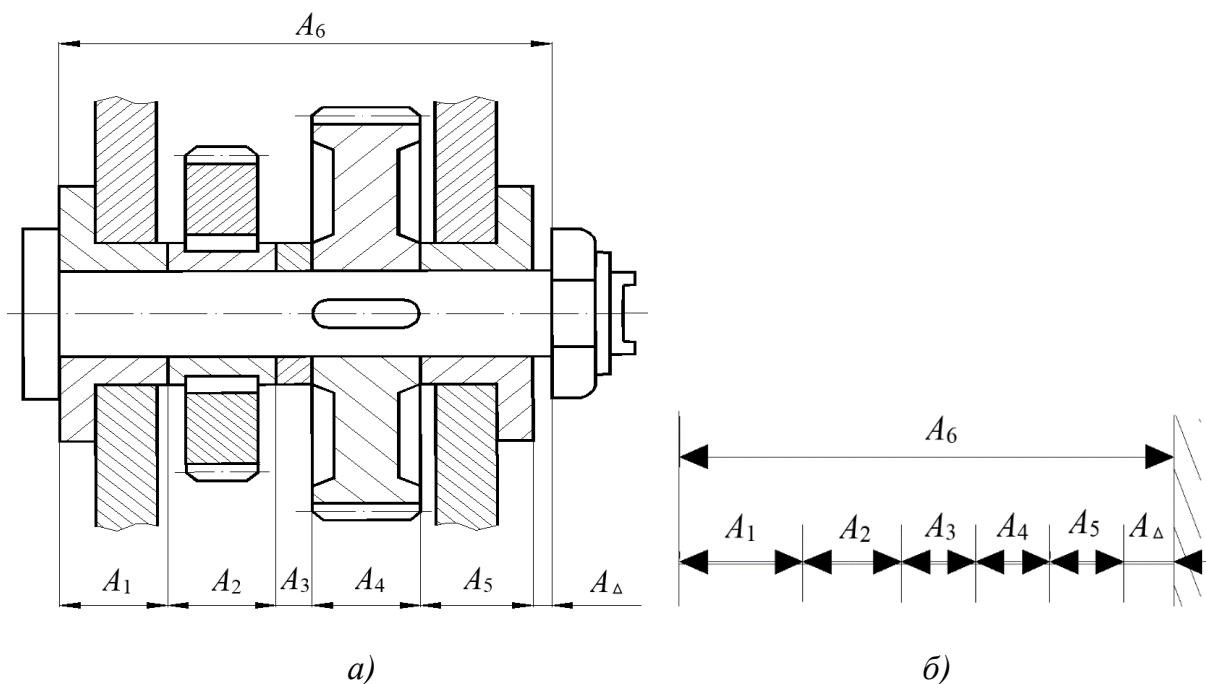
Формирование размерной цепи: а – эскиз редуктора для размерной цепи; б – схема размерной цепи
